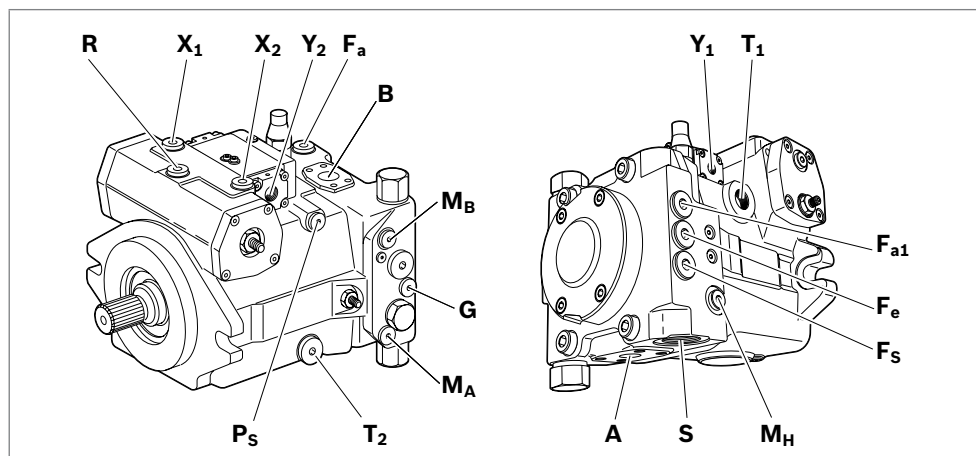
Vue d'ensemble des raccords A4VG, dimension nominale 40, 56
